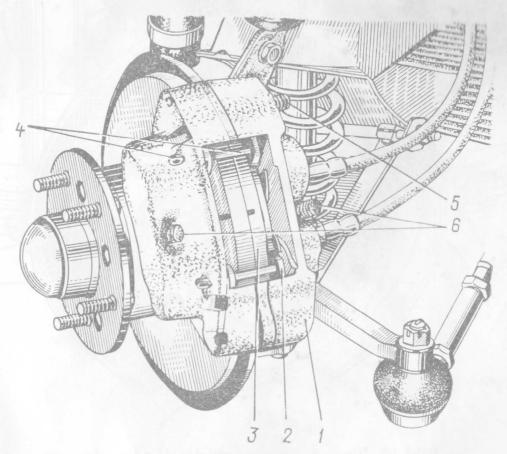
Vorderradscheibenbremse: 1 — Bügel; 2 — Bremsbacke; 3 — Bremsbelag; 4 — Splint; 5 — Luftauslaßventil an großem Zylinder; 6 — Luftauslaßventil an kleinen Zylinder
